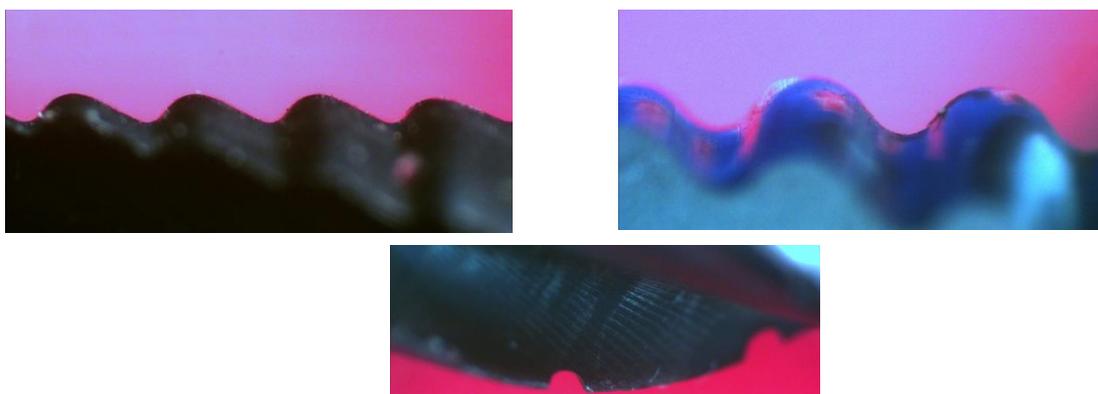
Профили режущих кромок фрез: *a* – асимметричный (Dormer); *б* – типа *WR* (Hahn-Kolb); *в* – типа *NF/HF* (Dormer)
